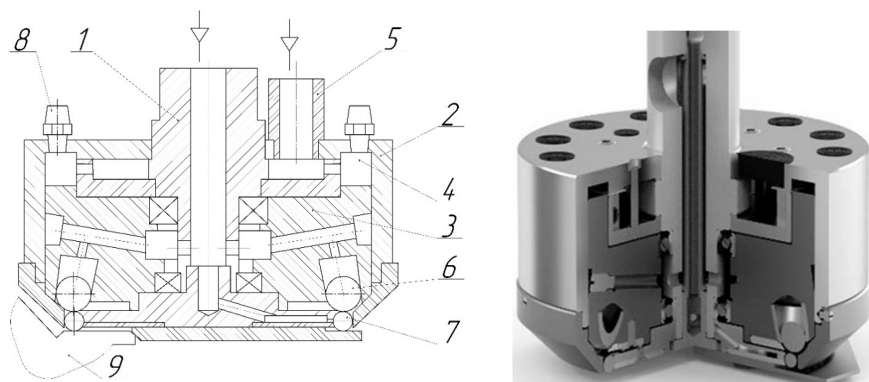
Инструмент для пневмоударной обработки плоских поверхностей из различных материалов: 1 – полый вал; 2 – корпус; 3 – диск; 4 – лопатки; 5 – штуцер; 6 – приводящие шары; 7 – деформирующие шары; 8 – пневмоглушители; 9 – заготовка
